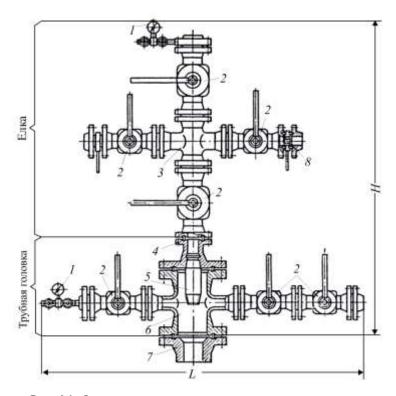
Фонтанная арматура крестового типа с крановыми запорными устройствами: I — манометр; 2 — кран (задвижка); 3 — крестовик елки; 4 — переводная катушка (трубная головка); 5 — патрубок для подвески НКТ; 6 — крестовик трубной головки; 7 — фланец колонной головки; 8 — штуцер
